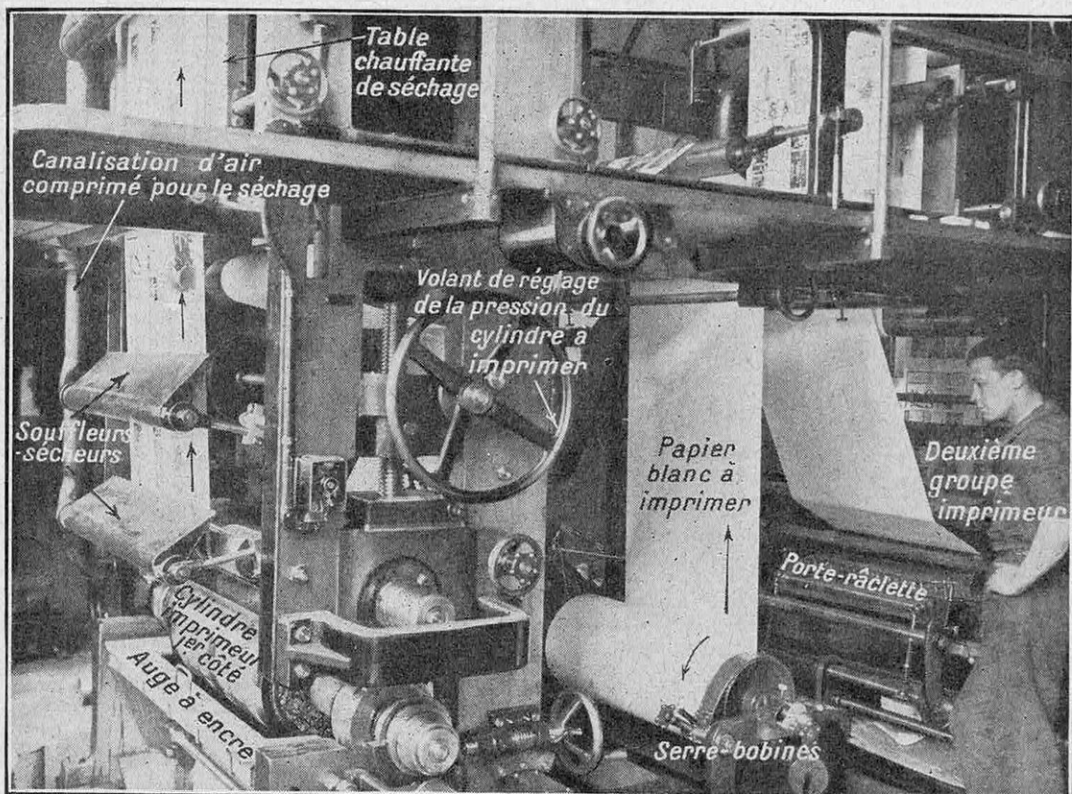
VUE D'ENSEMBLE DE LA PRESSE A IMPRIMER SUR PAPIER EN BOBINE
